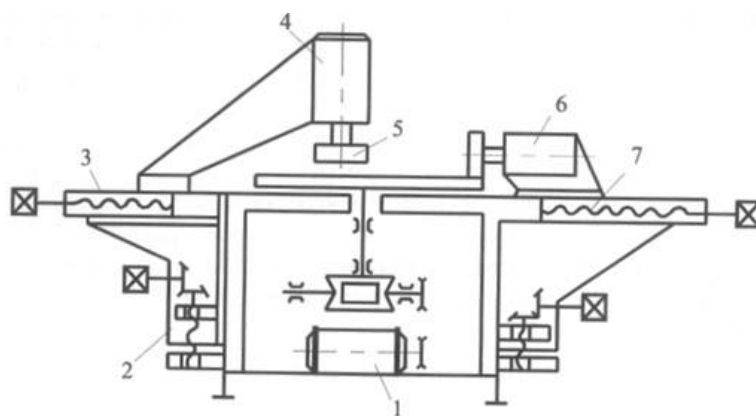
схема установки для полірування дисків компресора сизалевими кругами.
